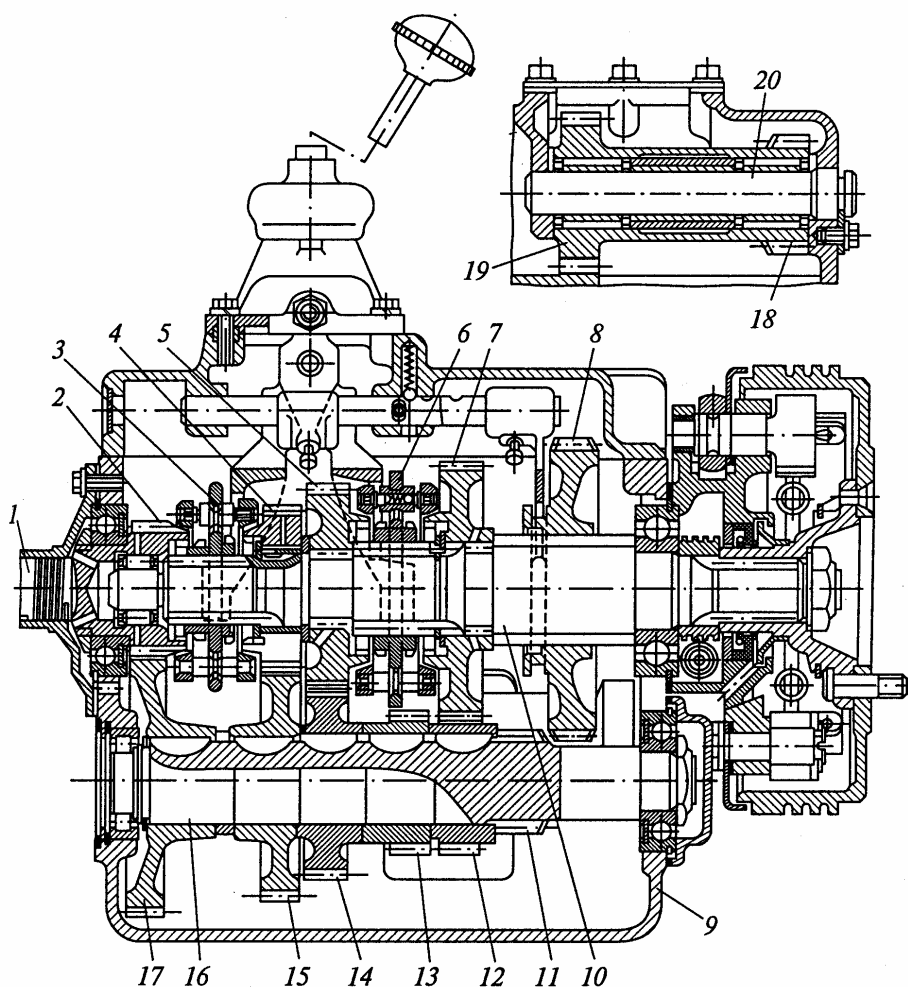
Коробка передач грузовых автомобилей ЗИЛ:
